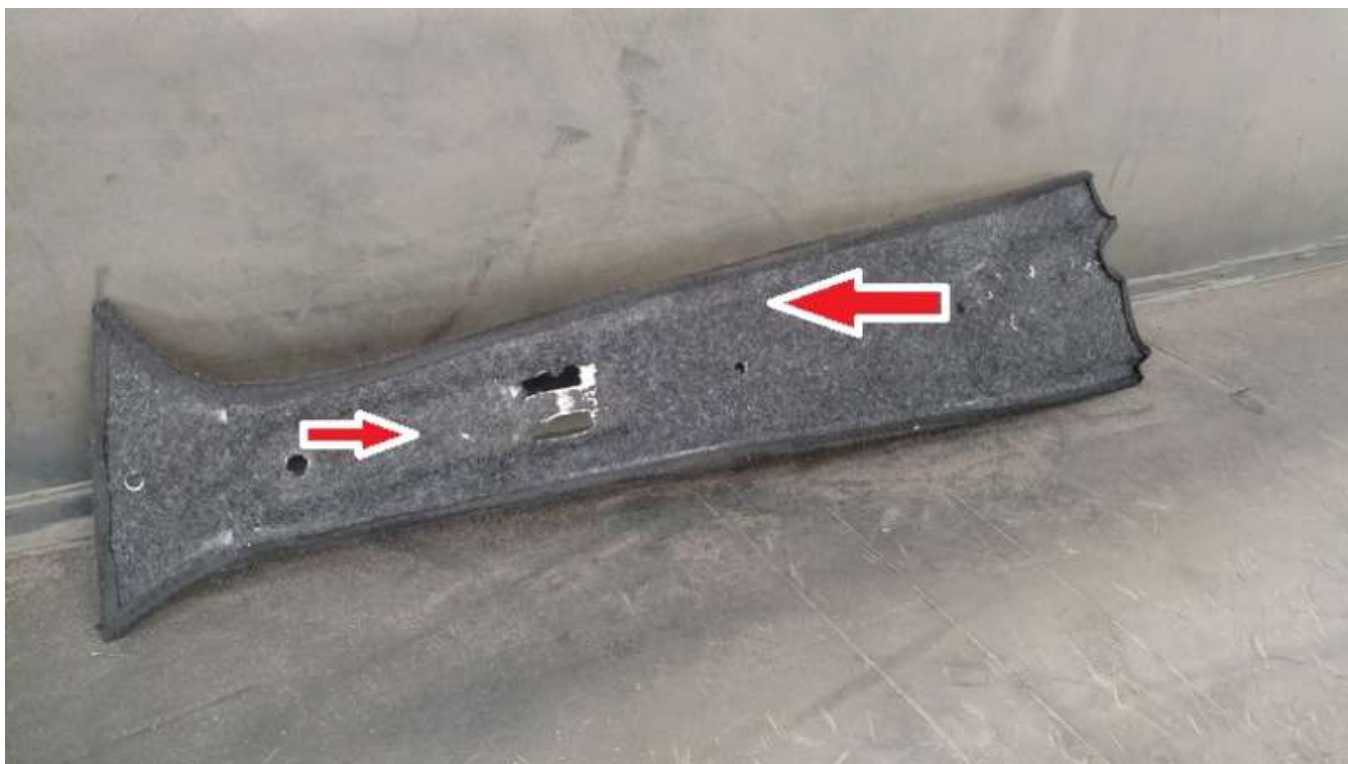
Detalhe do carpete aplicado na face oposta da chapa de aço
